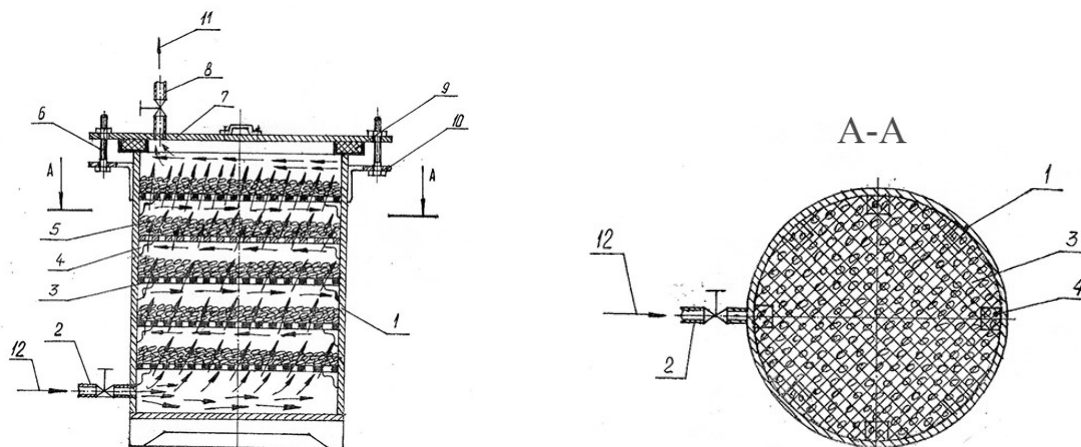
Устройство очистки биогаза: 1 – корпус устройства; 2, 8 – газовые трубы; 3 – сетчатая перегородка; 4 – перегородки; 5 – цеолитовые минералы; 6 – разъем; 7 – крышка; 9 – уплотнитель; 10 – соединительные опоры; 11 – чистый газ; 12 – смешанный газ
